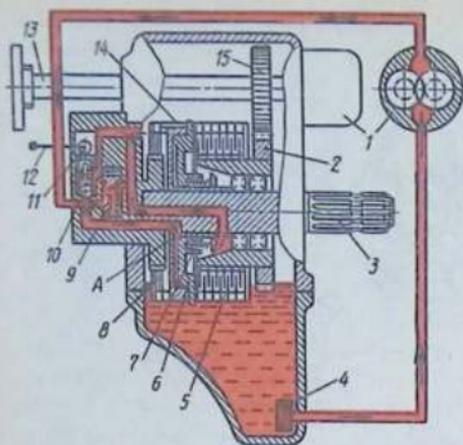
Схема редуктора ВОМ трактора Т-150К:
